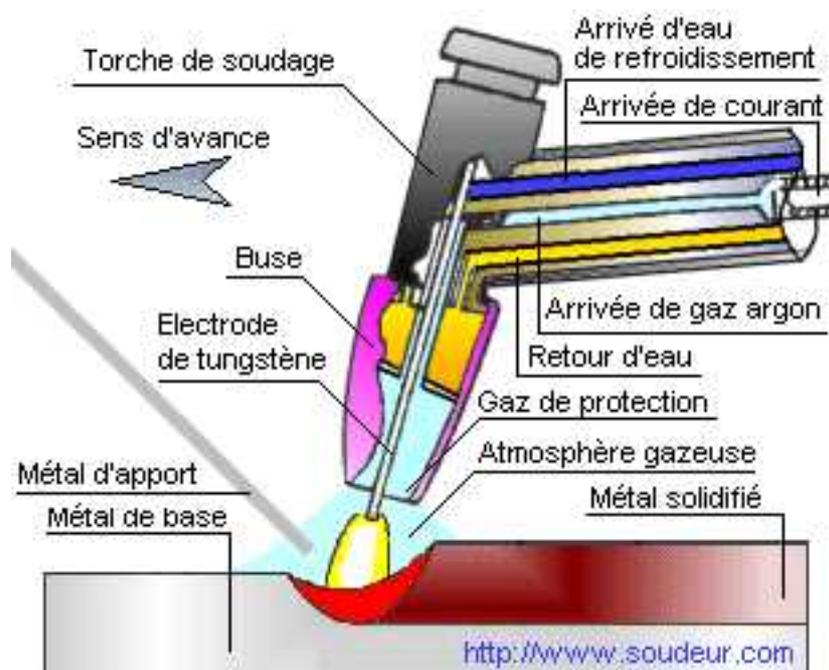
Principe de la soudure "TIG" (Image soudeur.com)
